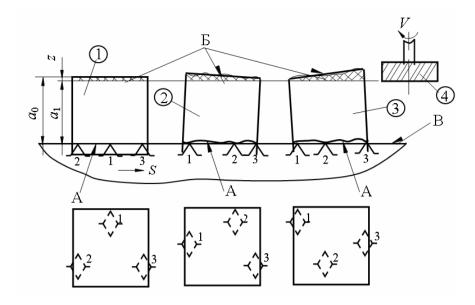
Влияние макрорельефа базовой поверхности А заготовки на неравномерность снимаемого припуска z: 1 — заготовка в виде идеального прямоугольного параллелепипеда; 2 — заготовки с реальным макрорельефом установочной ТБ; 4 — фреза; Б — поверхность заготовки до начала обработки; В — установочная поверхность приспособления; a_0 и a_1 — размеры заготовки соответственно до начала и после обработки
